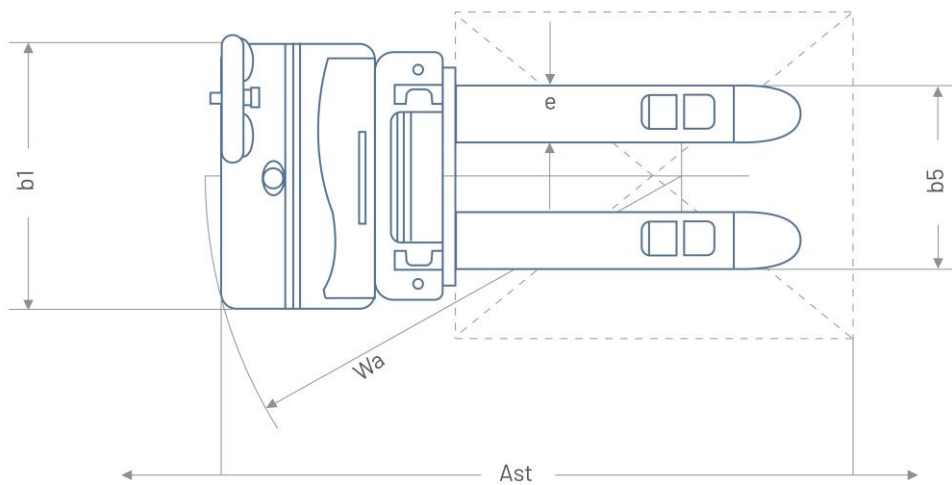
Draufsicht des SMART-S mit Kürzeln
